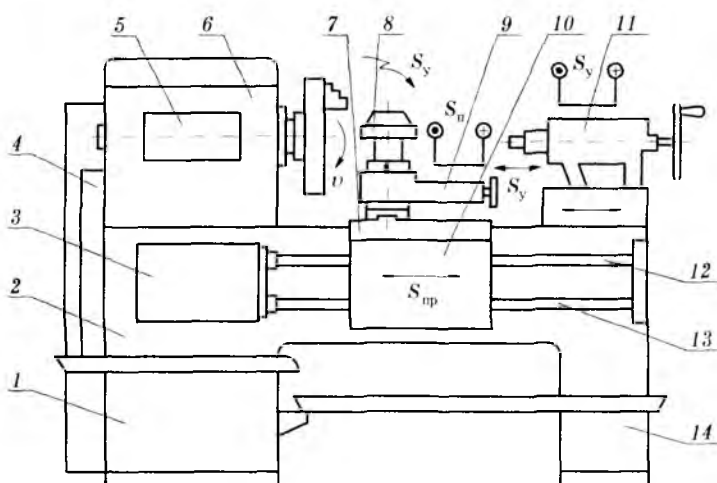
Общий вид токарно-винторезного станка 16K20
